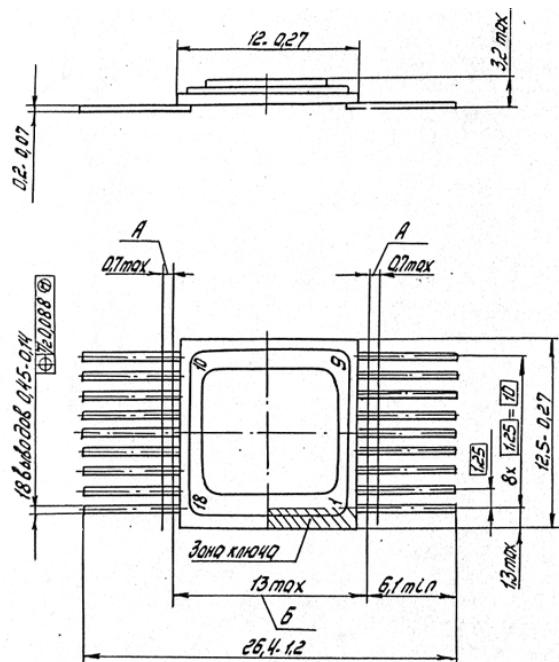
Габаритный чертеж корпуса 427.18-2.03
